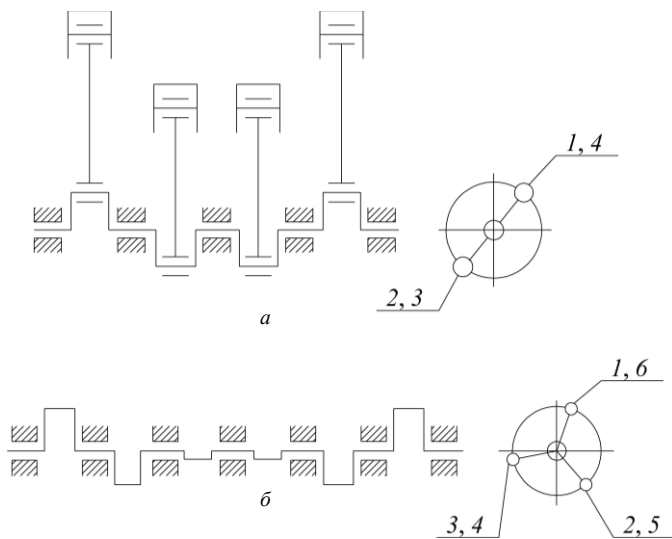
Схемы коленчатых валов двигателей, балансируемых без технологических втулок: *а* – 4-цилиндрового двигателя; *б* – 6-цилиндрового двигателя; *1-6* – номера кривошипов
